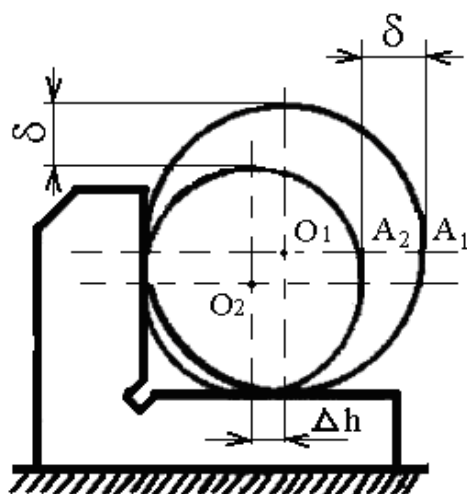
Схема образования погрешности базирования при установке детали в «координатный угол»
